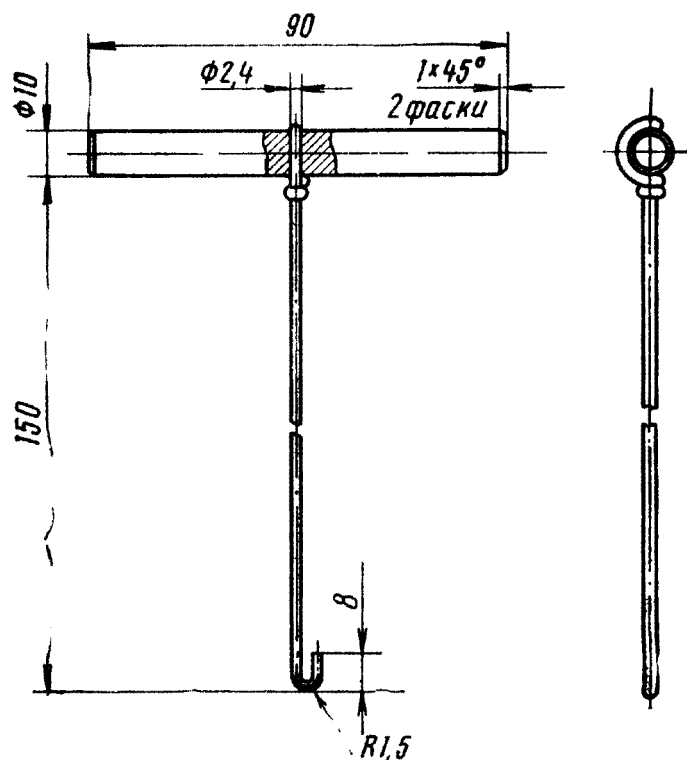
Крючок для демонтажа пружин синхронизатора коробки передач
